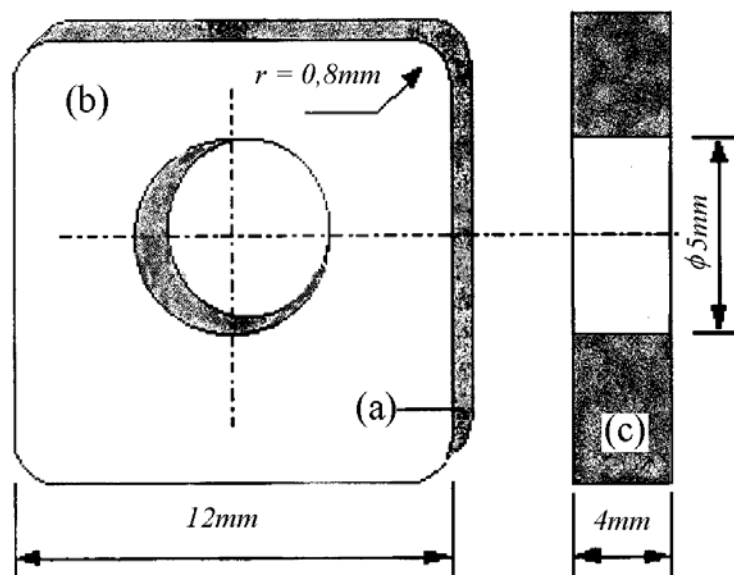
Principais dimensões da ferramenta de corte K10, onde (a) é a superfície de corte, (b) a superfície de saída e (c) a superfície de folga.<sup>b</sup>
